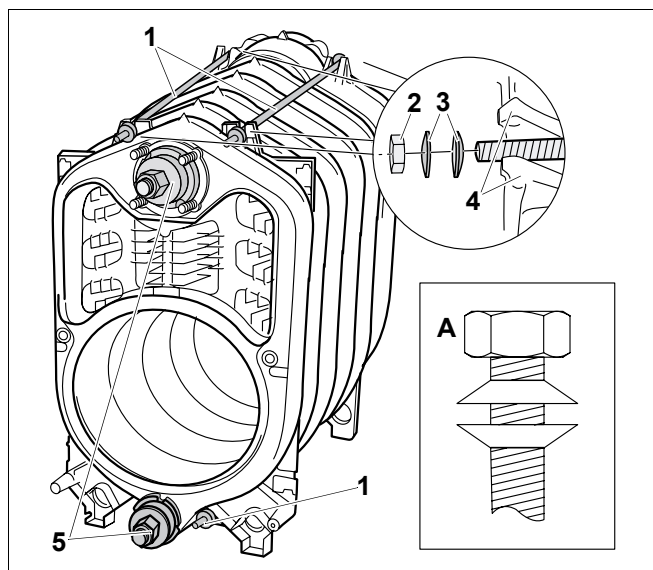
Установка анкерных штанг – расположение тарельчатых пружин
